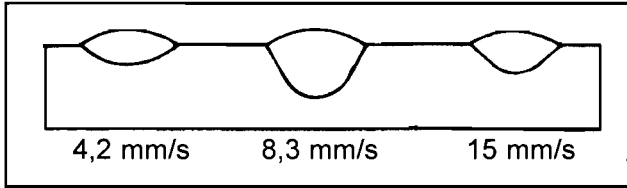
EFECTO DE LA VELOCIDAD DE SOLDEO EN EL ASPECTO DEL CORDÓN EN PROCESO AUTOMÁTICO
